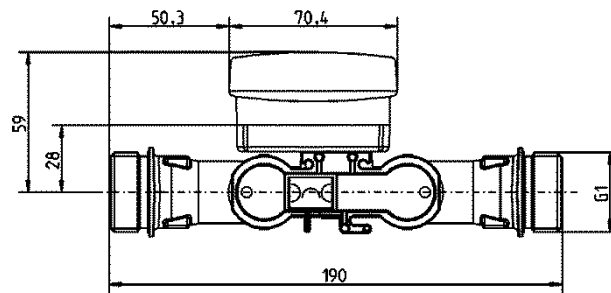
Dimensjoner ved byggelengde 190 mm (gjenget)
